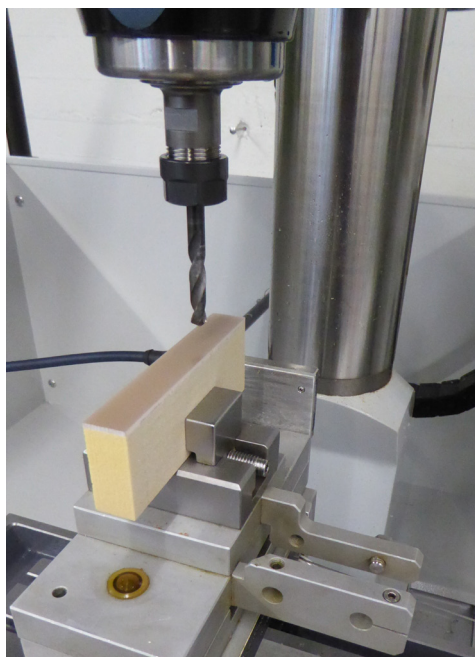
Aufbau des RMS-Bohrprüfstandes auf einer Werkzeugmaschine «Fehlmann Picomax 21-M»
